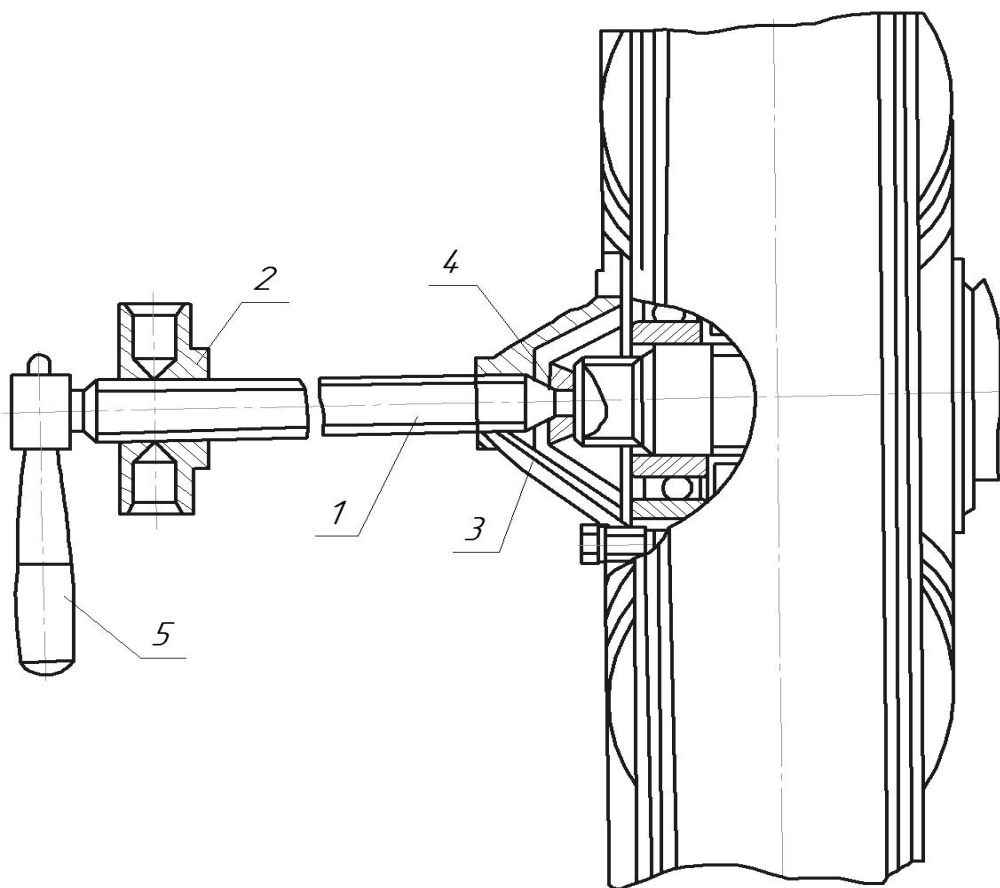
Демонтаж направляющего колеса и опорного катка:
